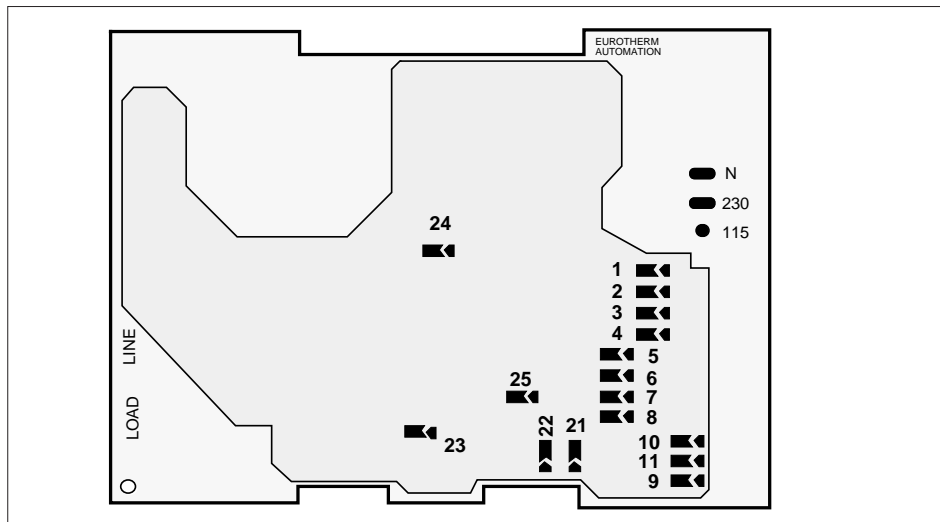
Carte électronique «Type 2» Emplacement des «grains de café» (vue côté soudures)
